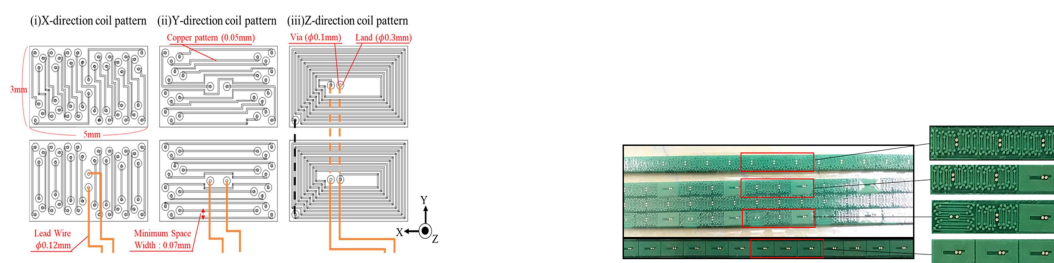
PCB コイルパターン (左)、PCB コイルアレイ (右)
